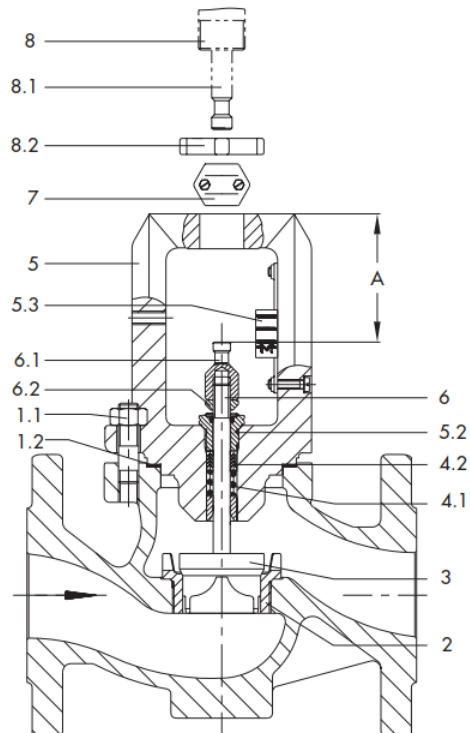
Регулюючий клапан типу 241-7, вид в розрізі.
